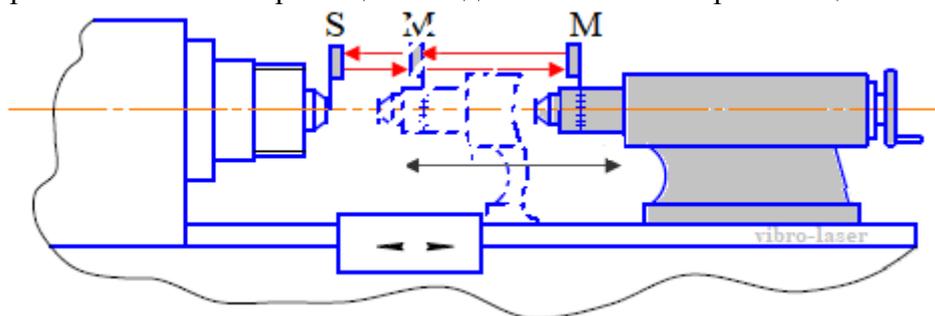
Установка лазерных головок S и M системы лазерной центровки
